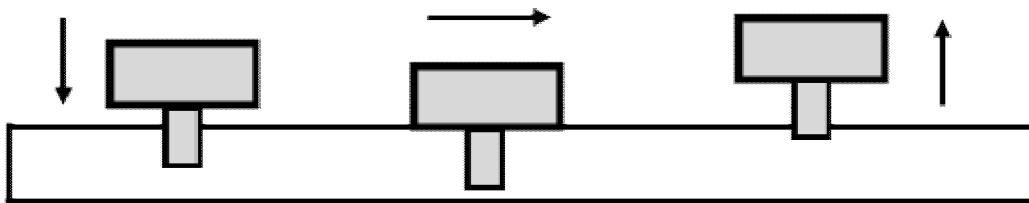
Principe général du procédé de soudage par friction malaxage
